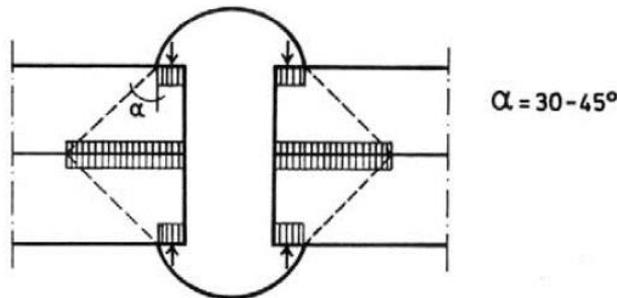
Tension dans un assemblage avec rivet à chaud [3]
